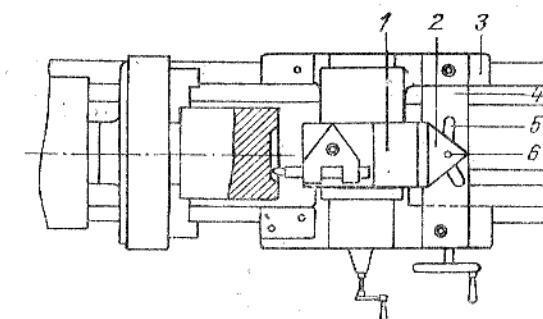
Strunjire prin copiere cu avans transversal:
